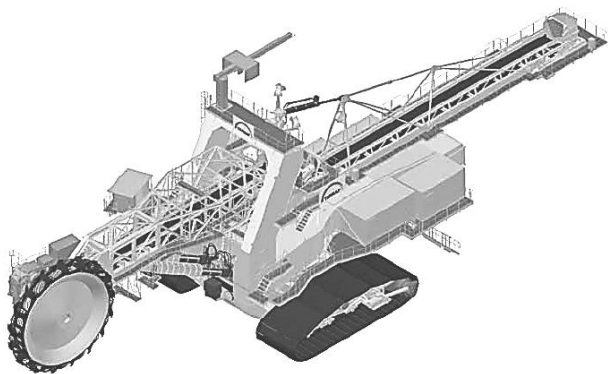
Общий вид роторного стрелового экскаватора
